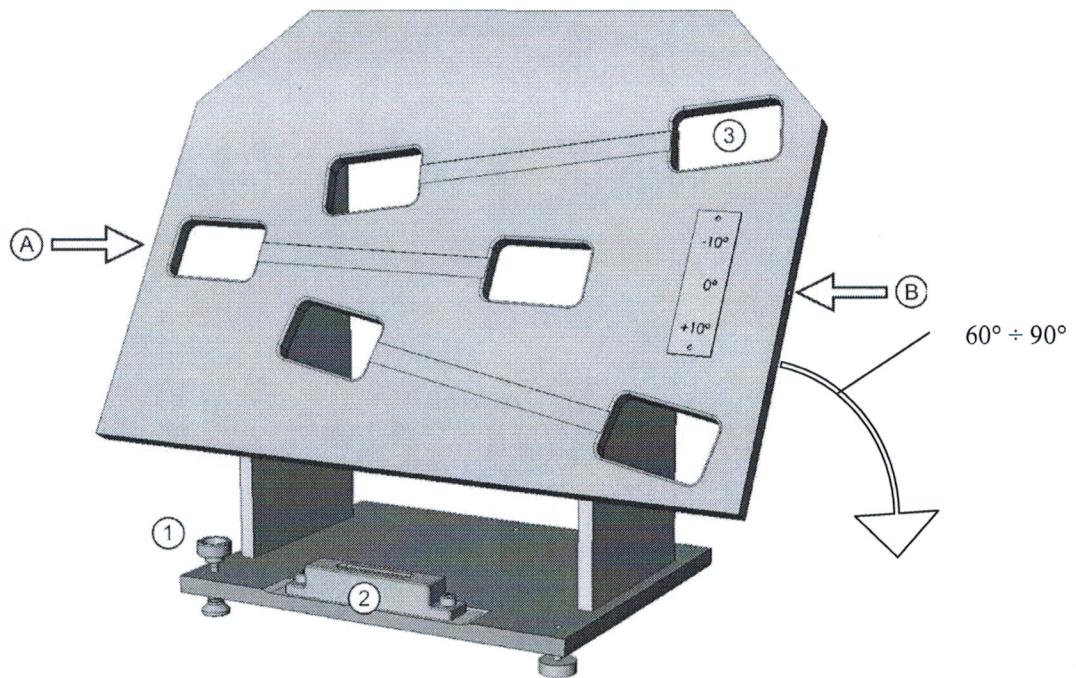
Калибровочное приспособление для имитации углов поворота рулевого колеса (1 - установочные винты; 2 – уровень; 3 - отверстия для зажимных рычагов; А / В - вспомогательные отверстия)
